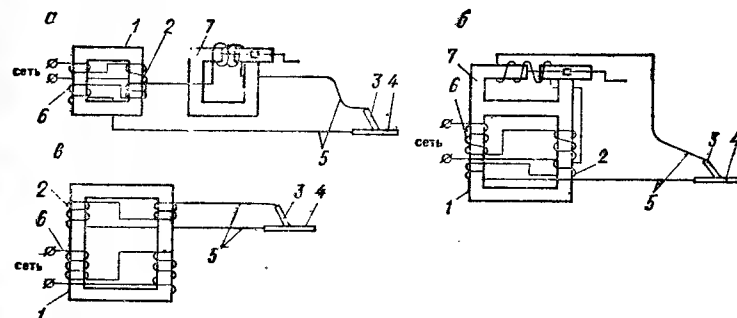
Схемы трансформаторов для дуговой сварки
